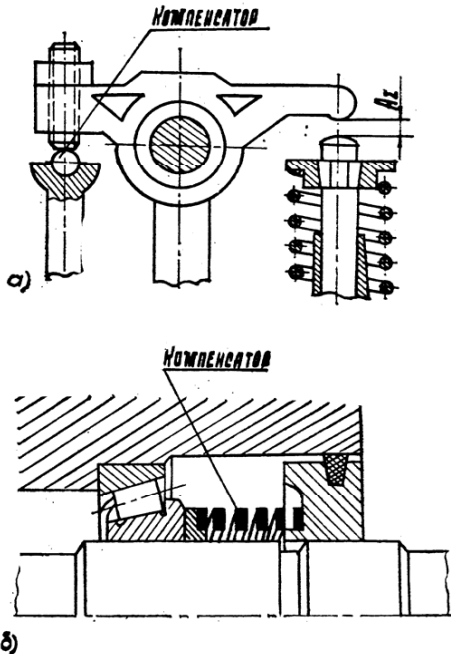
Компенсатори: а – ручний для регулювання зазору; б – автоматичний пружиний компенсатор
